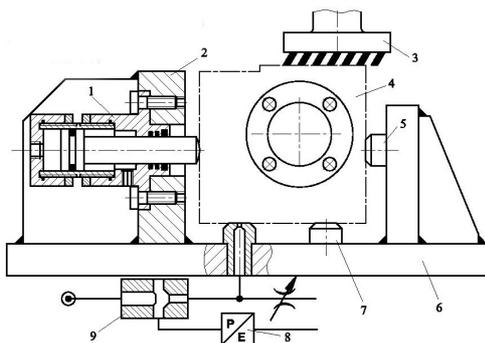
Vorrichtung zum Fräsen von Blockteilen
